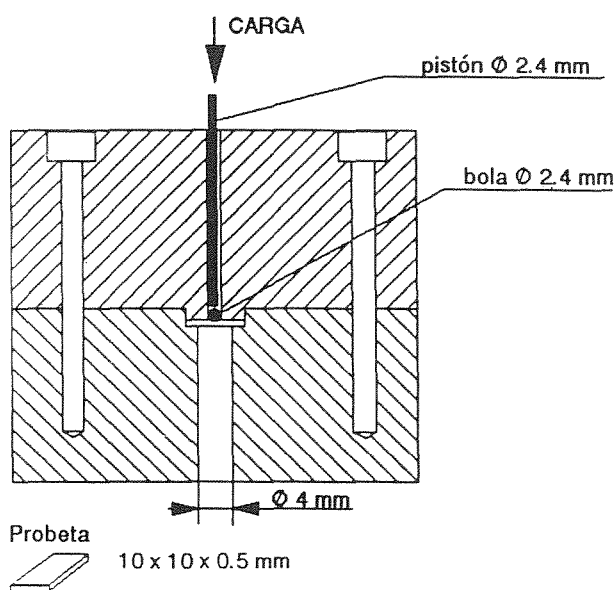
Soporte experimental empleado en los ensayos llevados a cabo utilizando la técnica SPT.
